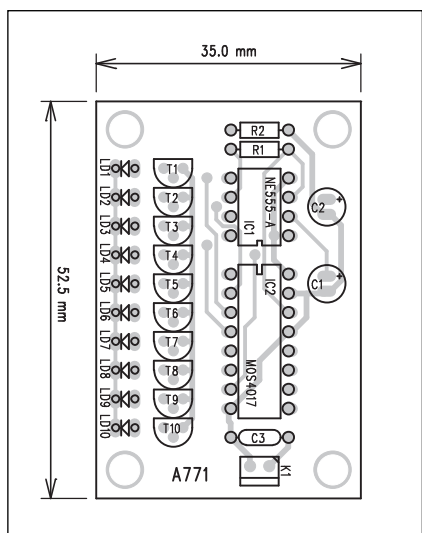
Deska spojů ze strany součástek (BOTTOM)
